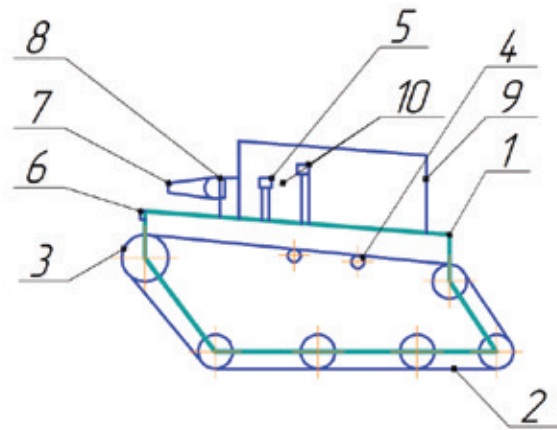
Конструкция робота: 1 — корпус; 2 — гусеница; 3 — направляющее колесо; 4 — ролик натяжителя гусеницы; 5 — камера (бортовая); 6 — камера (лицевая); 7 — брандспойт; 8 — манипулятор; 9 — защитная рама; 10 — лазерный термометр
